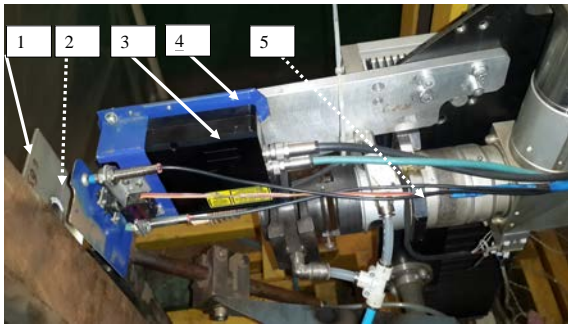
Макетний зразок системи пошуку місця зварювання: 1 – зразок, що зварюється; 2 – лінія, згенерована датчиком RiftekRF625; 3 – датчик RiftekRF625; 4 – кронштейни системи кріплення; 5 – лазерна зварювальна головка (частина)
